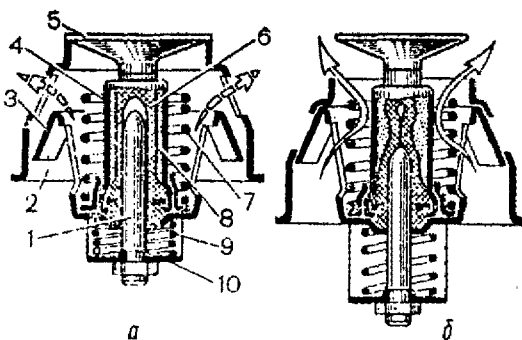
Устройство и работа клапана-термостата с твердым наполнителем: 1 – стержень; 2 – корпус; 3 и 5 – перепускной и основной клапаны; 4 – цилиндр; 6 – вставка; 7 и 9 – пружины; 8 – наполнитель; 10 – скоба; 11 – шток; 12 – компенсационная пружина
